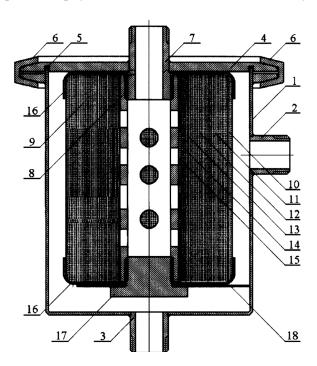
Схема фильтра для очистки жидкости, в частности для питьевой воды: 1 — корпус; 2 — входной штуцер; 3 — штуцер для слива промывной воды; 4 — крышка; 5 — резиновая прокладка; 6 — профильный хомут; 7 — выходной штуцер; 8 — опорная перфорированная трубка; 9 — фильтрующий элемент; 10...15 — слои фильтрующих материалов; 16 — крышка; 17 — пробка; 18 — центрирующая пластина
